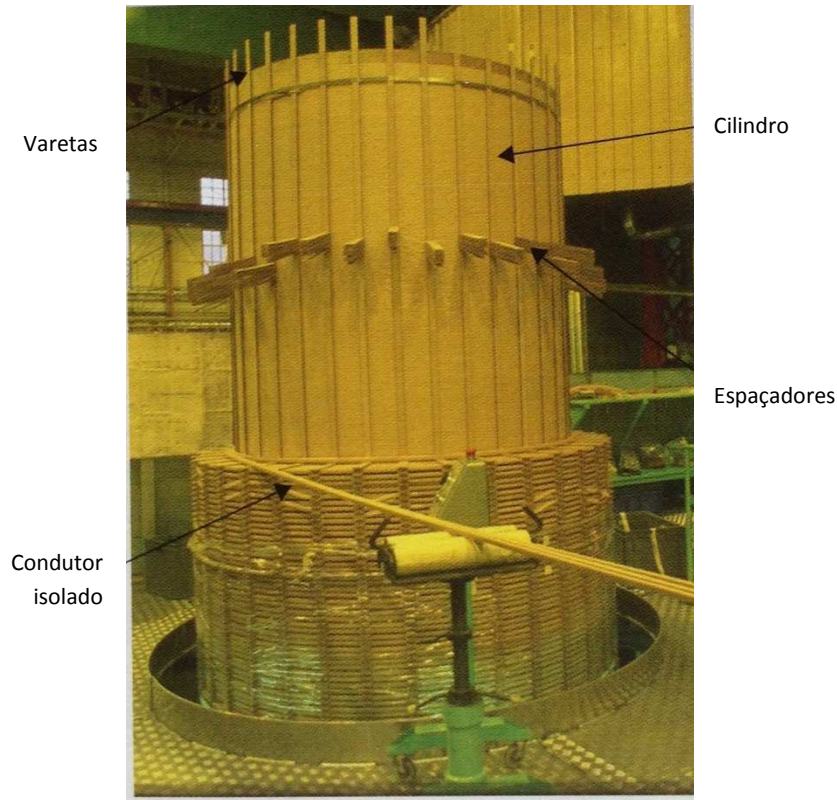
4– Fotografia de montagem de bobina – Fabricante D
